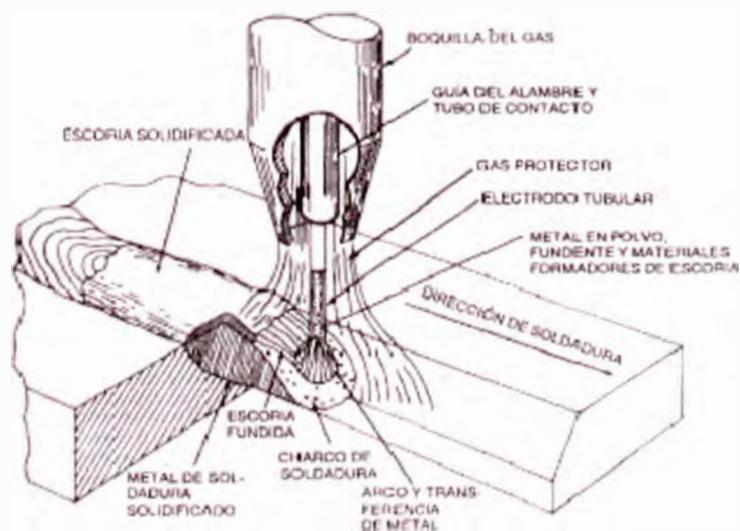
Esquema del proceso de soldadura FCAW
